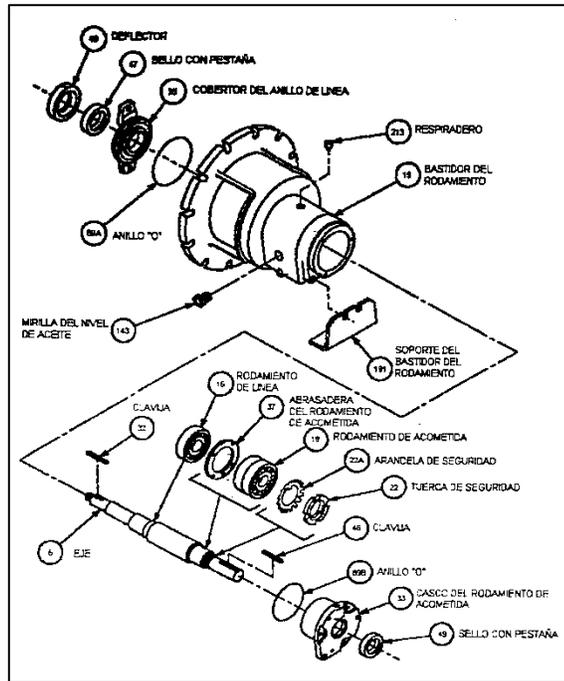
Despiece soporte rodamientos bomba Worthington 6FRBH-223.
